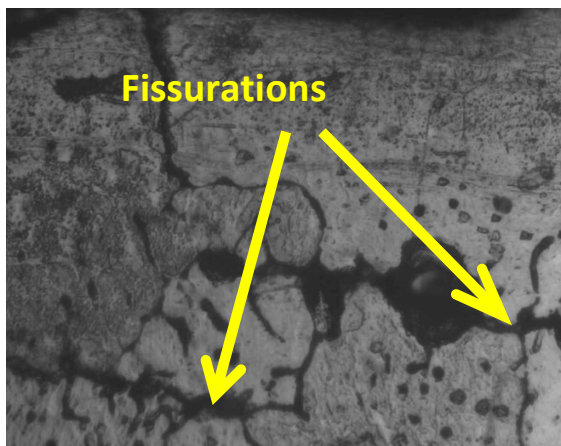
fissurations au niveau de la zone de liaison GX50
